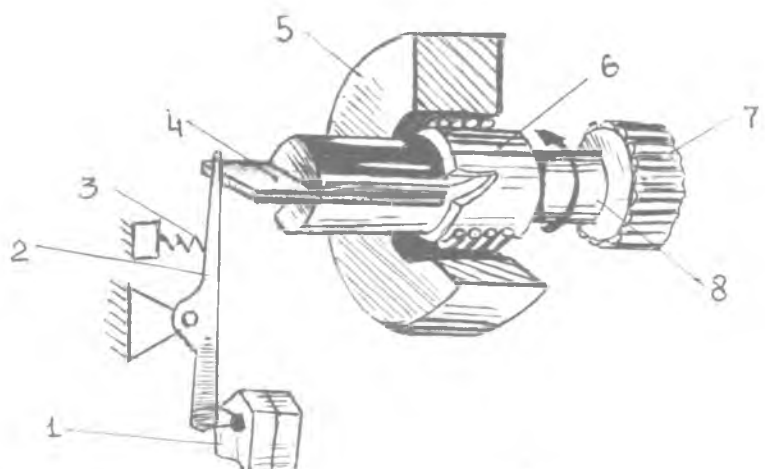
Инерционный датчик: 1 - микровыключатель, 2 - двойная качалка, 3 - возвратная пружина, 4 - толкатель; 5 - маятник, 6 - втулка, 7 - шестерня, 8 - вал.
